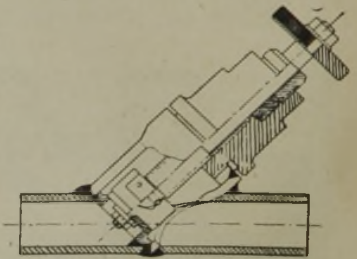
Vinidur-Schrägsitzventil NW 32 in Schweißkonstruktion, Aufbau.
